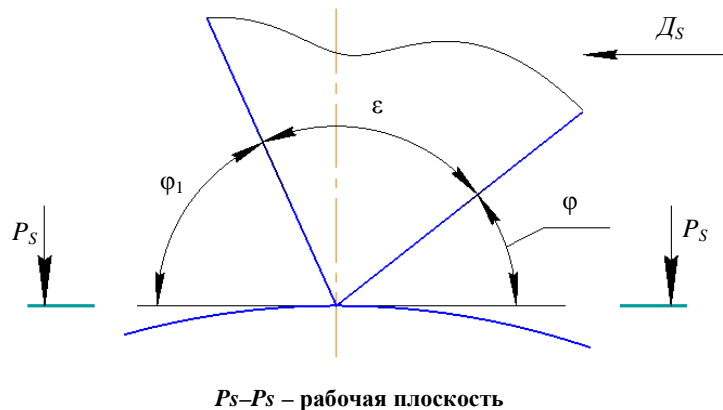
Расположение углов лезвия режущего инструмента φ , ε , φ_1 на сферической поверхности
